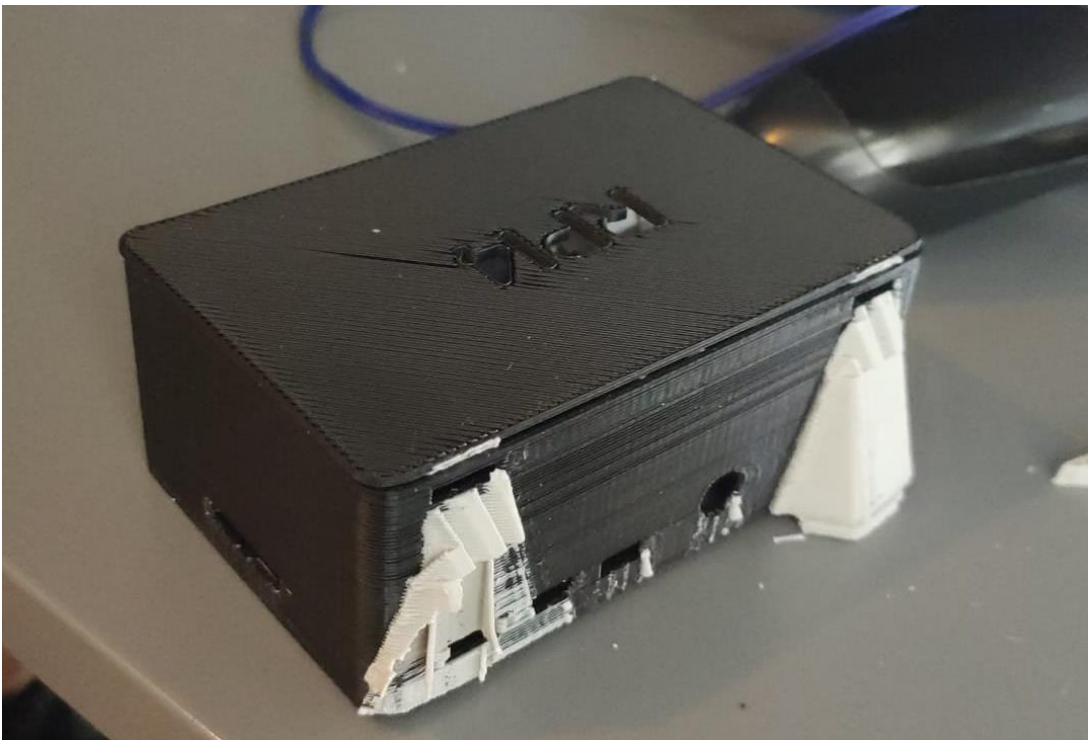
Das 3D-gedruckte Gehäuse Ansicht 2
